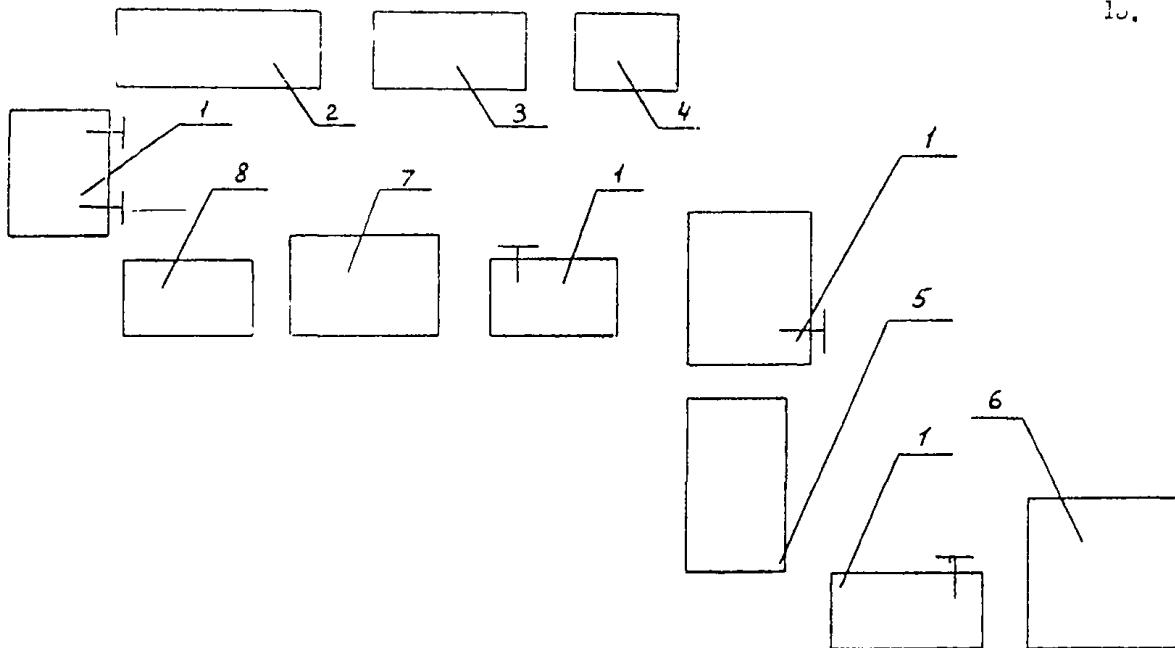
Типовая схема планировки рабочего места разборки и сборки
